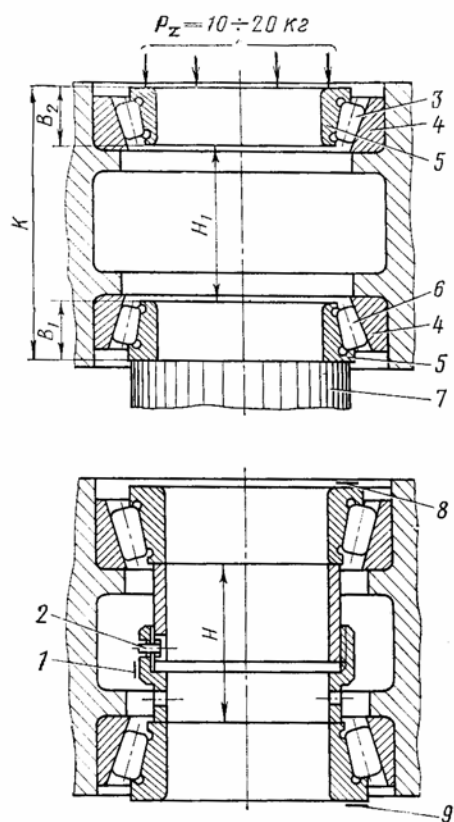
Регулировка распорной втулки и маркировка ее и подшипников: 1—место маркировки распорной втулки; 2—штифт; 3—верхний роликовый подшипник; 4—наружное кольцо подшипника; 5—внутреннее кольцо подшипника; 6—нижний роликовый подшипник; 7—подставка; 8, 9—места маркировки подшипников; B_1, B_2 —ширина нижнего и верхнего внутренних колец подшипников; K —расстояние между наружными плоскостями внутренних колец; H_1 —зазор между внутренними кольцами подшипников; H —длина распорной втулки; P_z —сила прижатия колец подшипника
